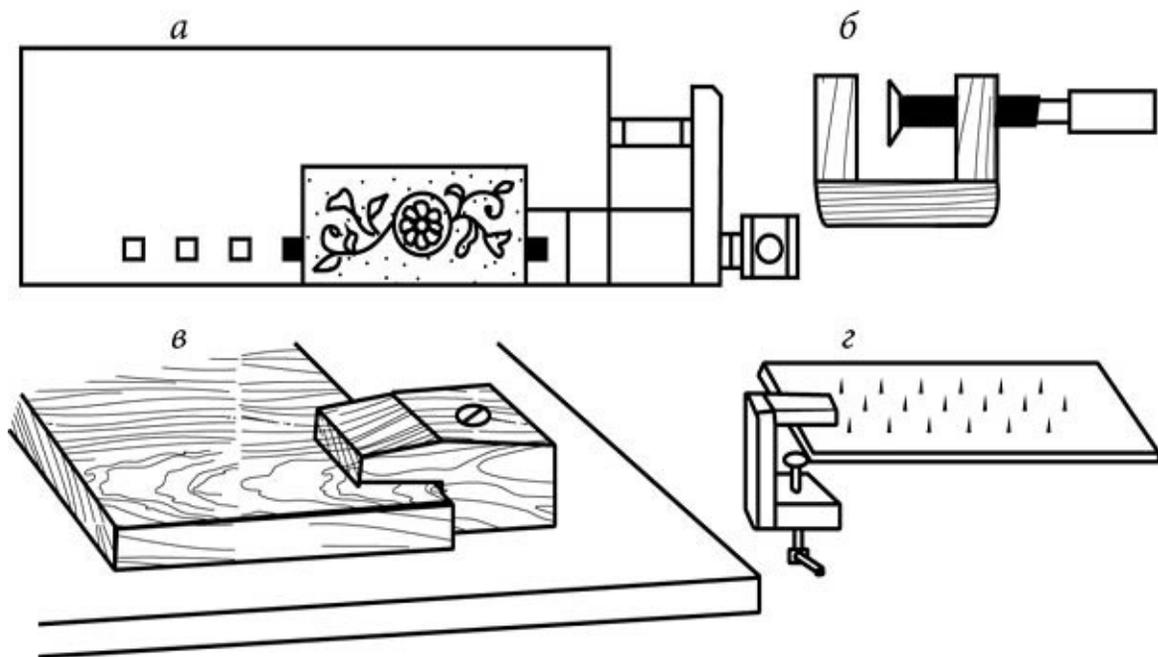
Приспособления для крепления заготовки: а – тиски столярного верстака; б – струбцина; в – державка; г – игольчатый держатель.
